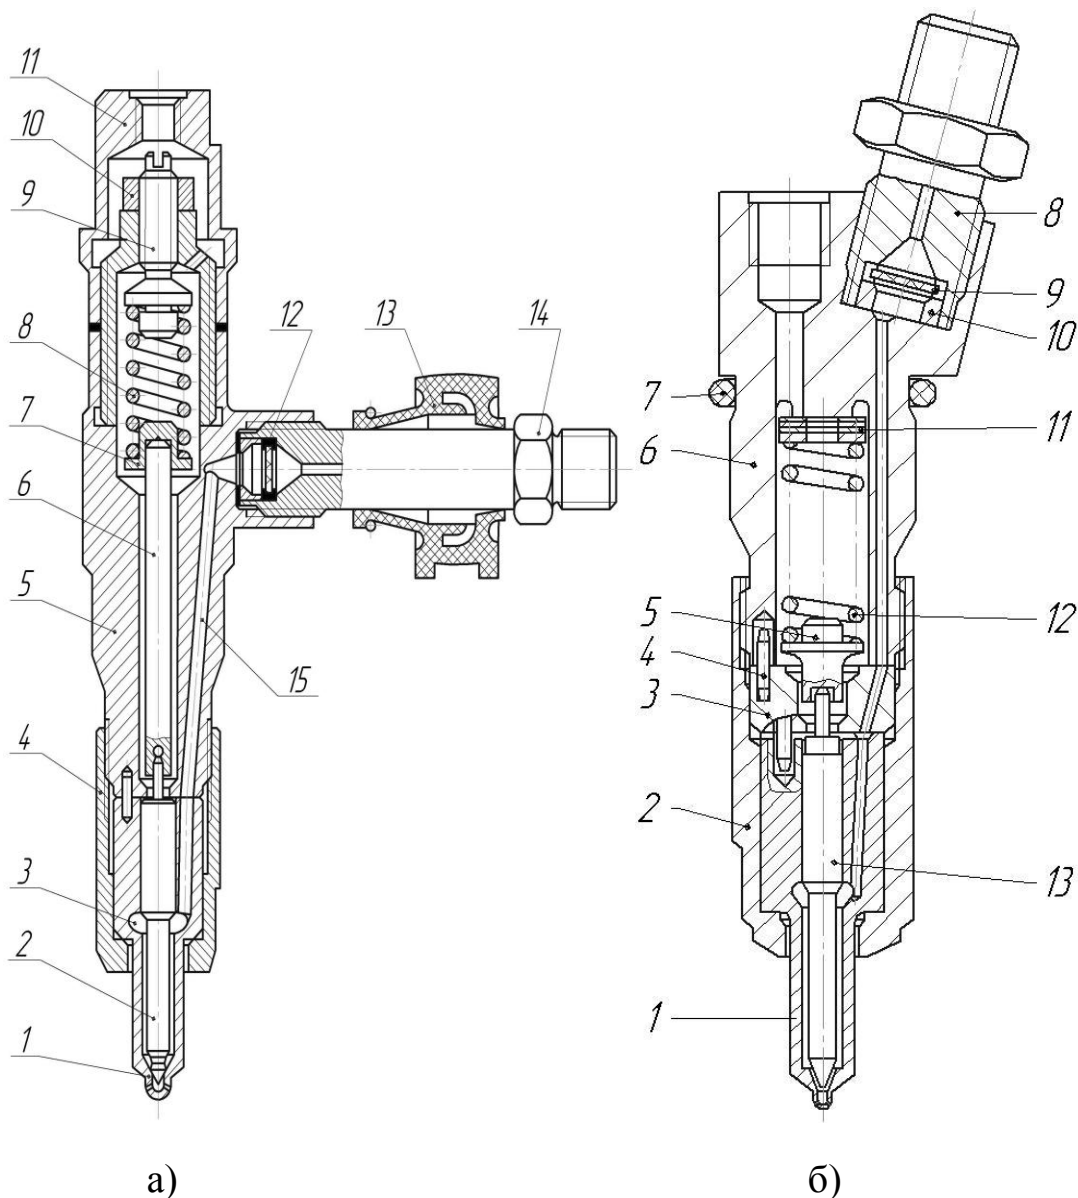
Форсунка штанговая (а): 1 – сопловые отверстия; 2 – игла; 3 – корпус распылителя; 4 – гайка распылителя; 5 – корпус; 6 – шток; 7 – опорная шайба; 8 – пружина; 9 – регулировочный винт; 10 – контргайка; 11 – колпак; 12 – сетчатый фильтр; 13 – уплотнитель; 14 – штуцер; 15 – канал
